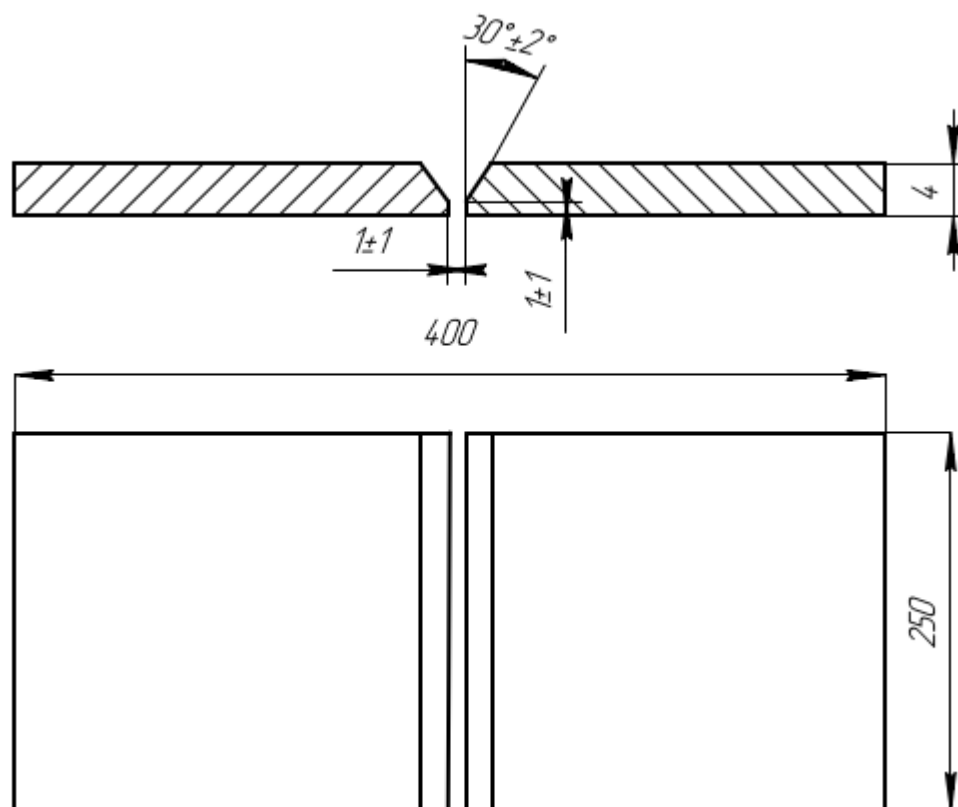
Геометрические параметры сборки пластин под сварку
